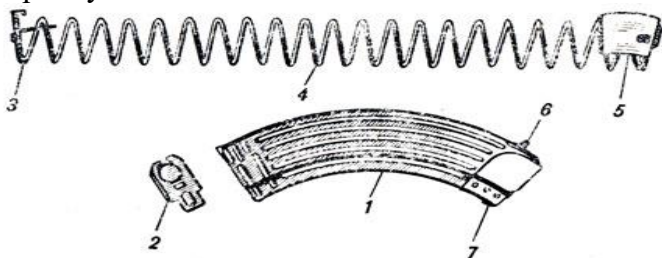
Магазин: 1 - корпус; 2 - крышка; 3 - стопорная планка; 4 - пружина; 5 - подаватель; 6 - опорный выступ; 7 - зацеп
